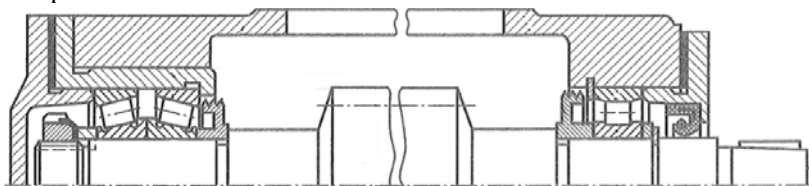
Вариант конструкции подшипникового узла с одной плавающей и одной фиксирующей опорой с двумя подшипниками для червячного вала
